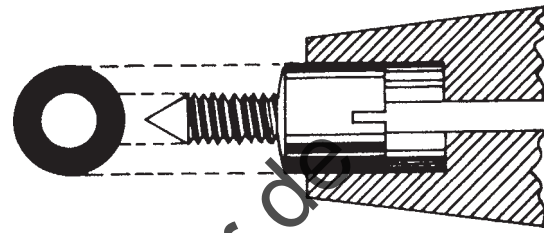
Eine gut passende Unterlegscheibe ist beinahe unsichtbar
